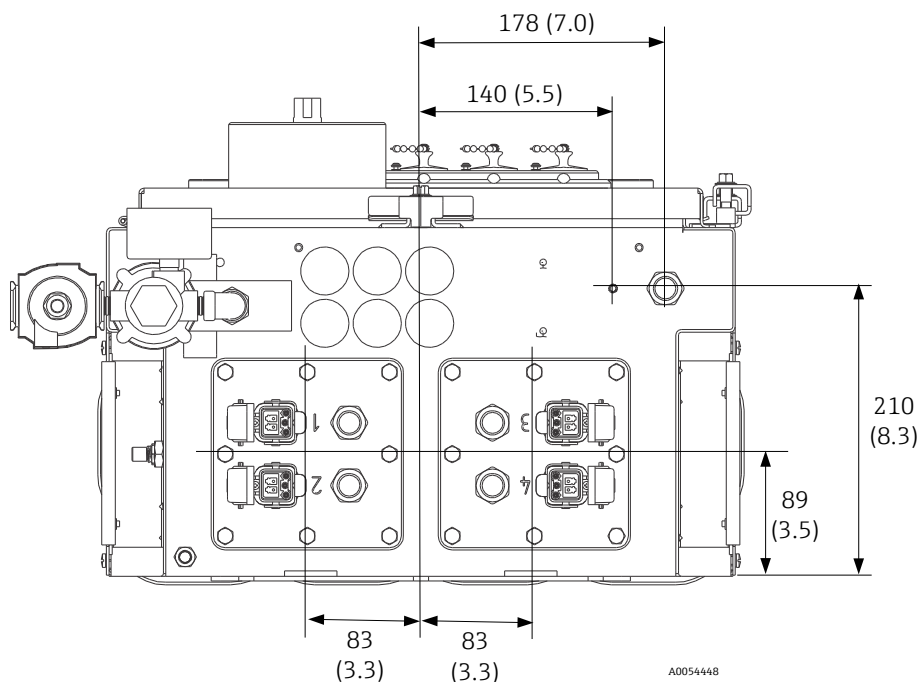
Vue de dessous du Raman Rxn5. Dimensions : mm (in)
